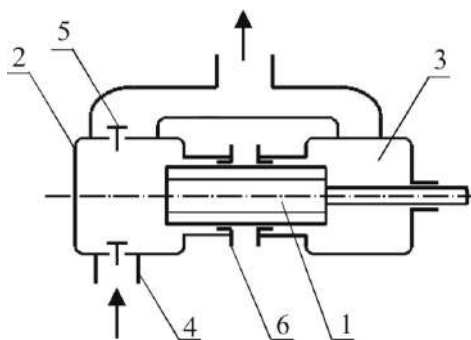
Дифференциальный плунжерный насос: 1 – плунжер; 2, 3 – цилиндры; 4, 5 – всасывающий и нагнетательный клапаны; 6 – сальниковые уплотнители.
